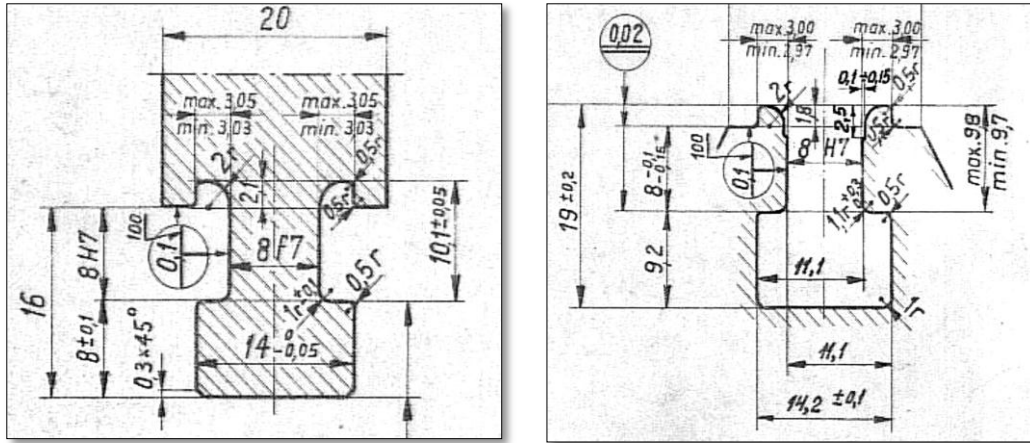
dimensioni del piede palare e della cava sul disco del 4° stadio della turbina n° 3.
